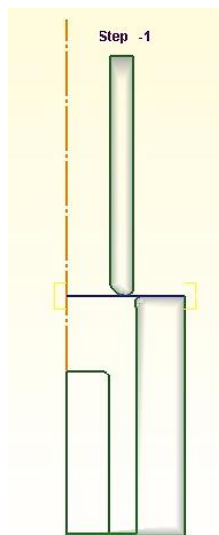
Схема реверсивной вытяжки за 1 ход пресса
